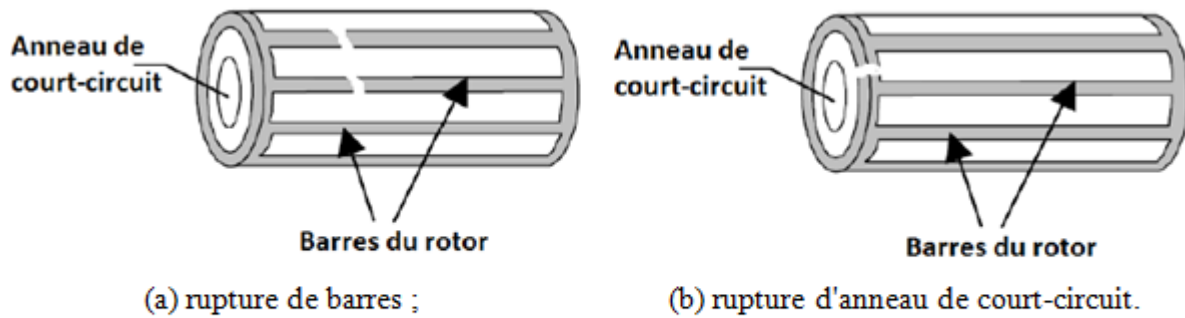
Défaut d'un rotor à cage d'écureuil
